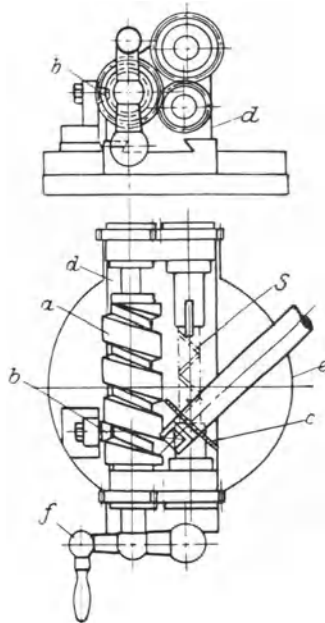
Fräsvorrichtung zum Fräsen kleiner Leitspindeln für Füllfederhalter.
